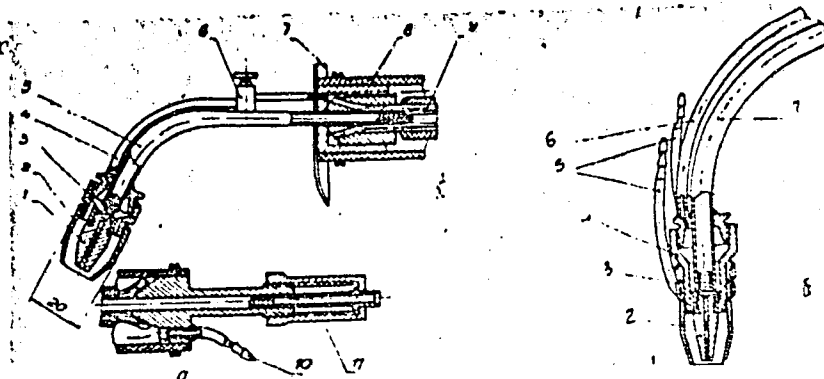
Держатели для полуавтоматической сварки:
